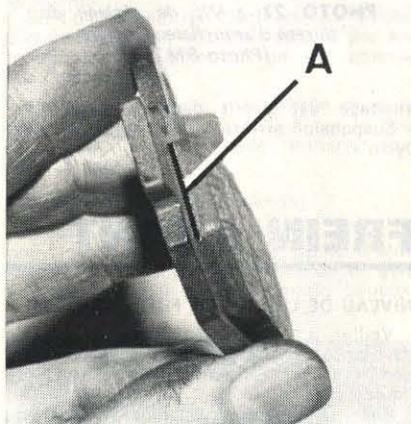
Trait de limite d'usure de plaquette (Photo RMT)
